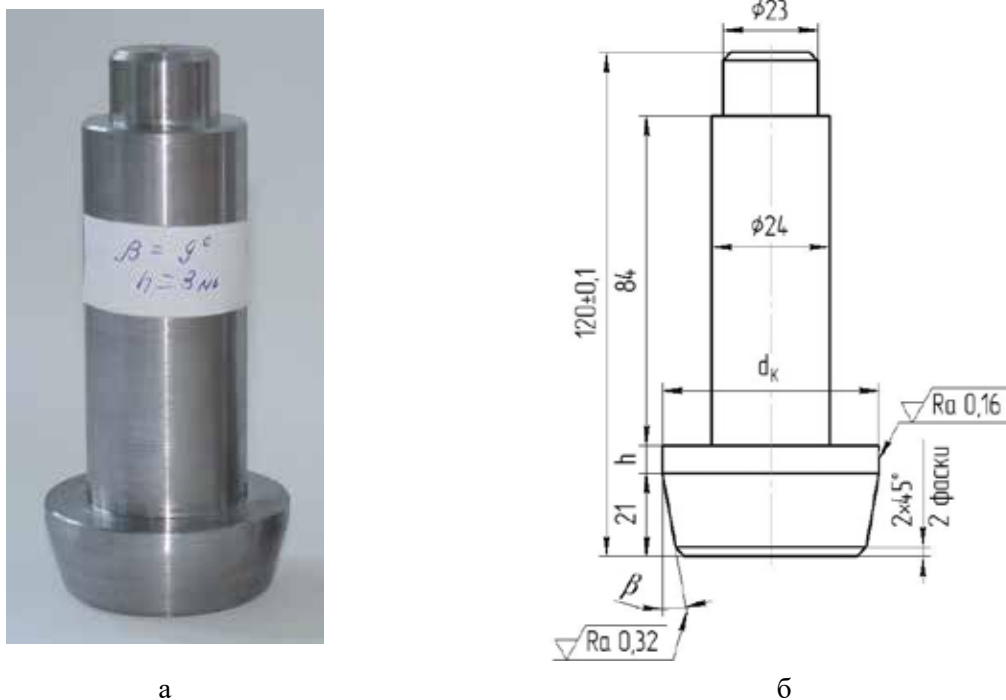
Пуансон, що використаний для обробки робочих поверхонь бронзових втулок автомобільних двигунів: а – натурний зразок; б – компоновальна схема [13]
